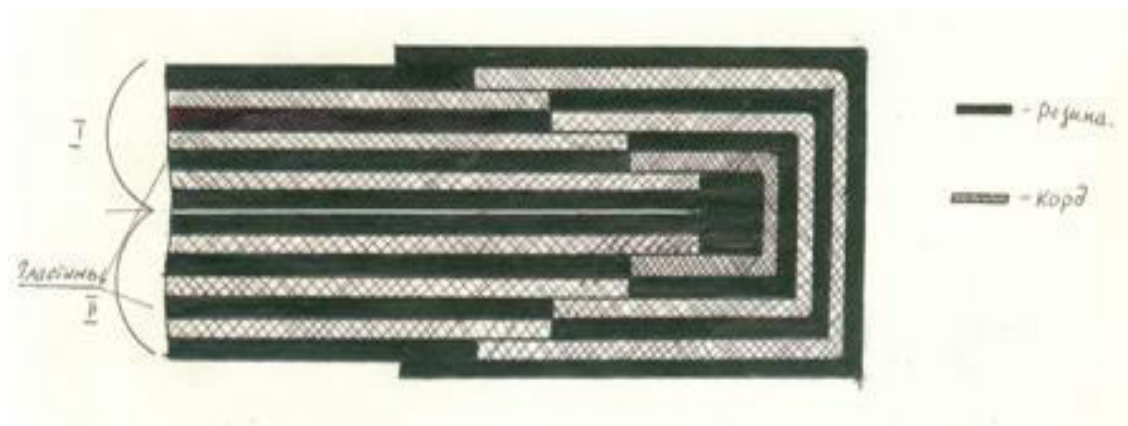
Схема сборки пневмобаллона из резиновых заготовок.
